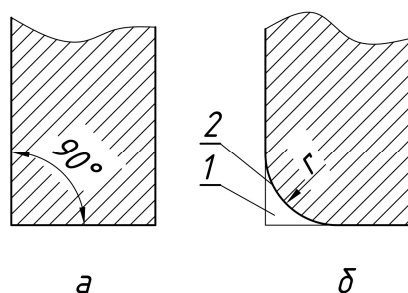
Профиль рабочей поверхности плоского ножа:
